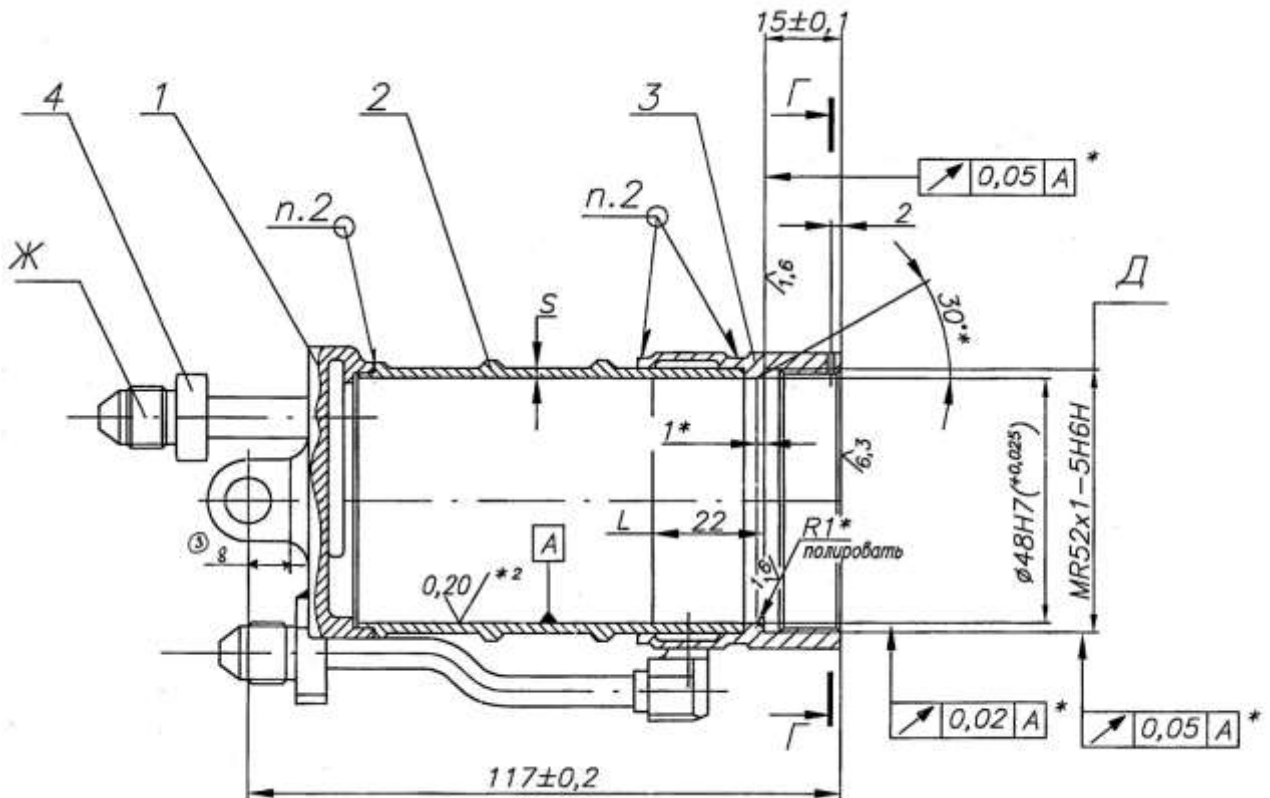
Чертеж ГЦ с требованиями по точности изготовления и качеству поверхностей
